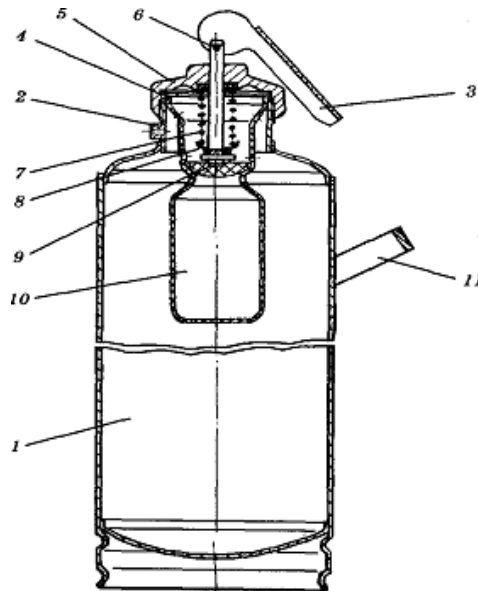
Вогнегасник хімічно-пінний ВХП-10: 1 – корпус; 2 – сприск; 3 – важіль запуску; 4 – кільце ущільнювальне; 5 – кришка; 6 – шток; 7 – пружина; 8 – шайба упорна; 9 – клапан; 10 – стакан; 11 – ручка
